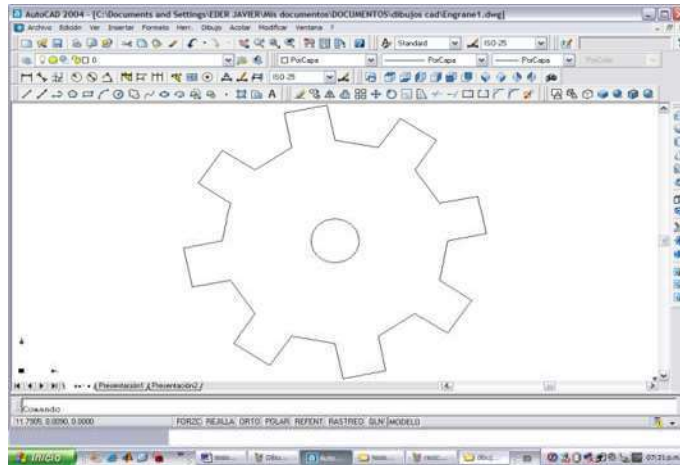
Dibujo a manufacturar diseñado en AutoCAD 2004
